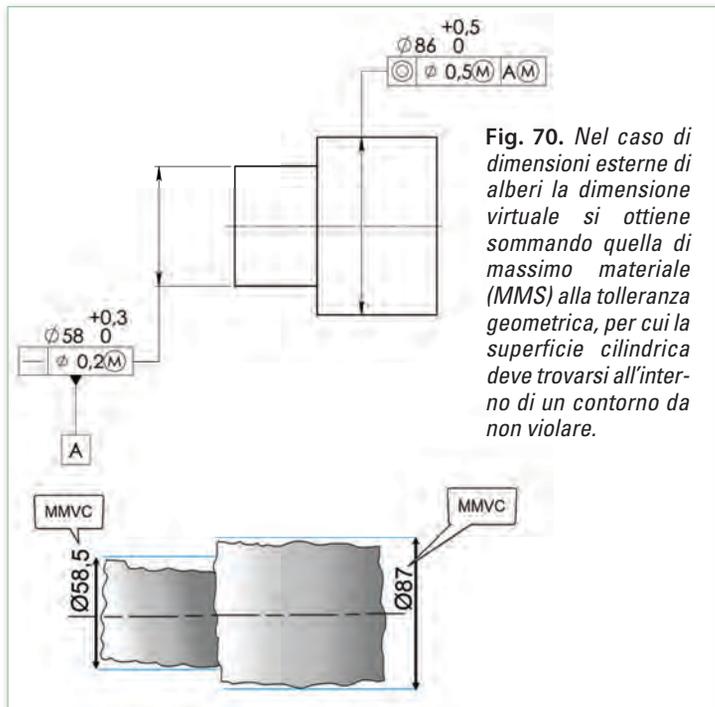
Nel caso di dimensioni esterne di alberi la dimensione virtuale si ottiene sommando quella di massimo materiale (MMS) alla tolleranza geometrica, per cui la superficie cilindrica deve trovarsi all'interno di un contorno da non violare.
